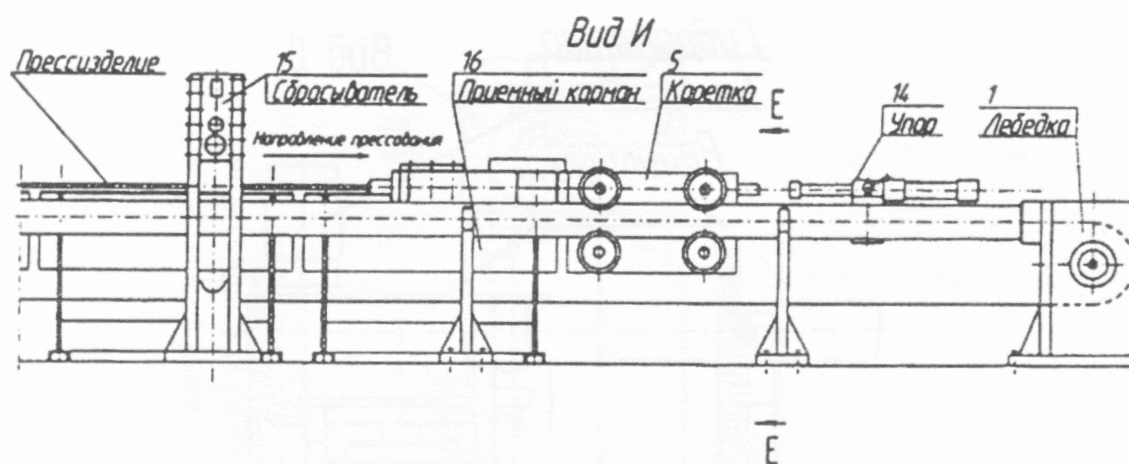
Передняя часть пуллера с установкой сбрасывателя
